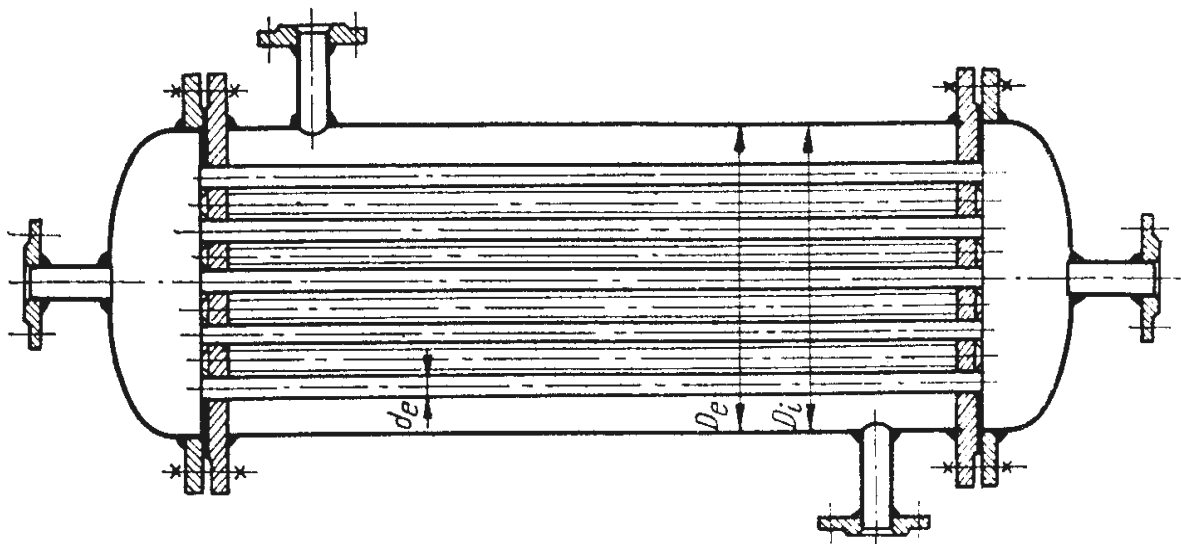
Schimbător de căldură cu fascicul de țevi în manta și plăci tubulare de capăt fixe.
